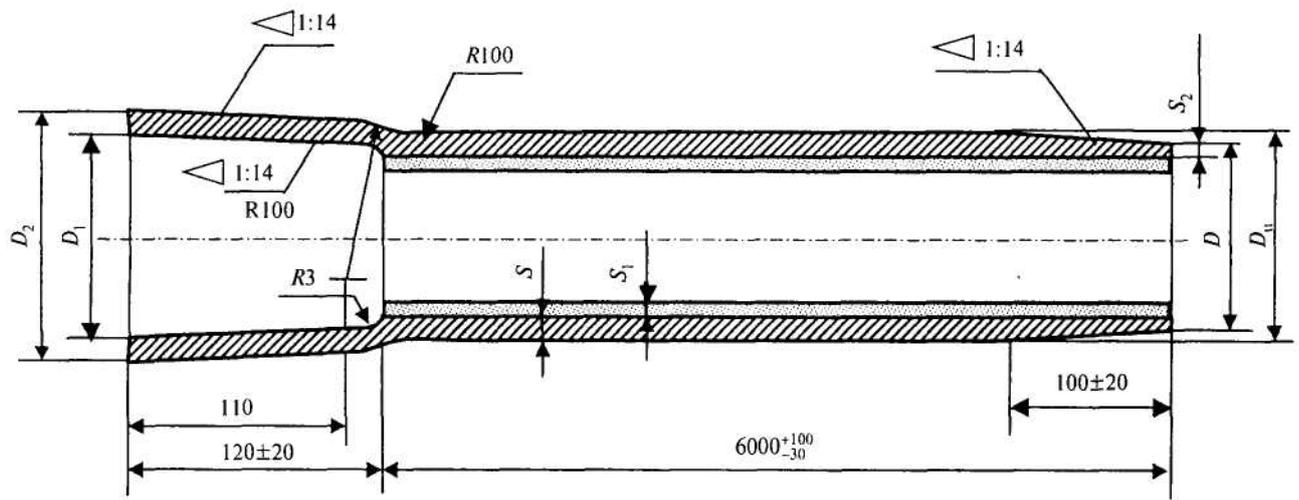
Схема трубы под нахлестное сварное соединение
